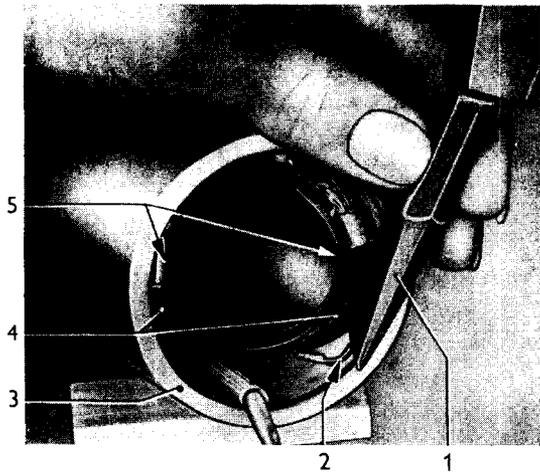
Punktschweißverbindung mit Meißel lösen
